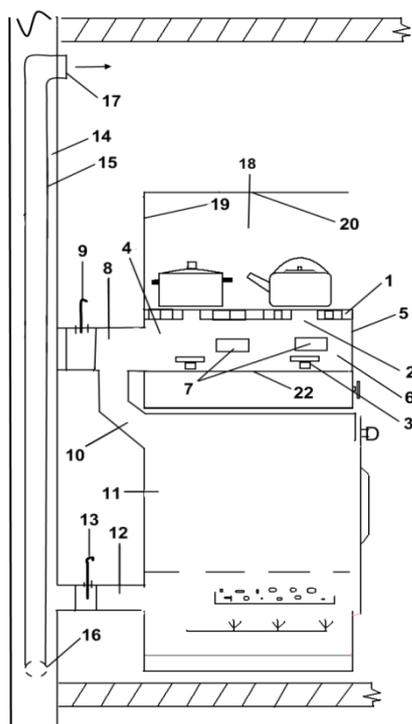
Конструкция бытовой газовой плиты: вид сбоку в разрезе
